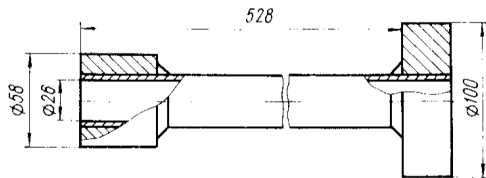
Подставка для запрессовки среднего подшипника с подушкой в сборе
